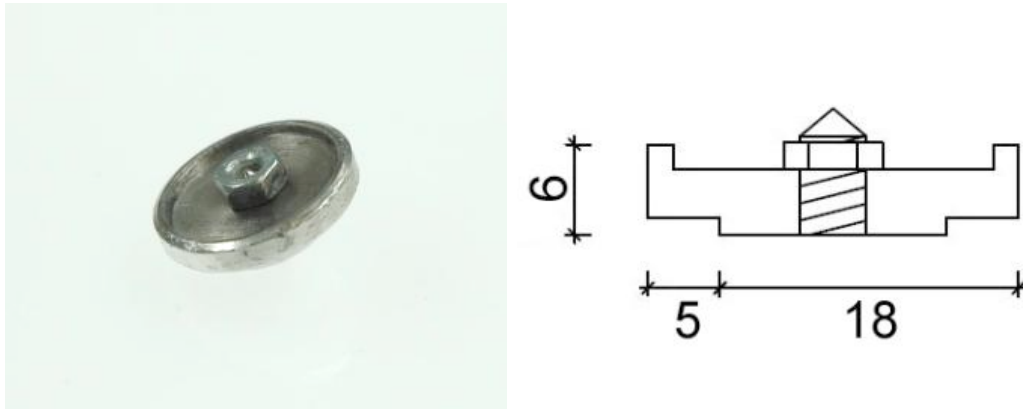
Socketteller aus Aluminium (Foto und Zeichnung)
